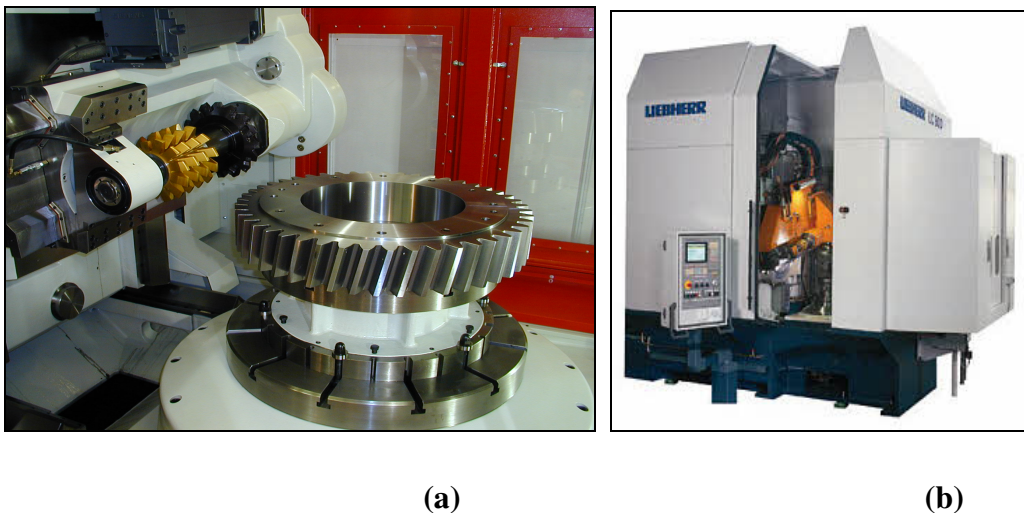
Máquina para geração por fresa caracol reto. a) Interno – b) Externo
